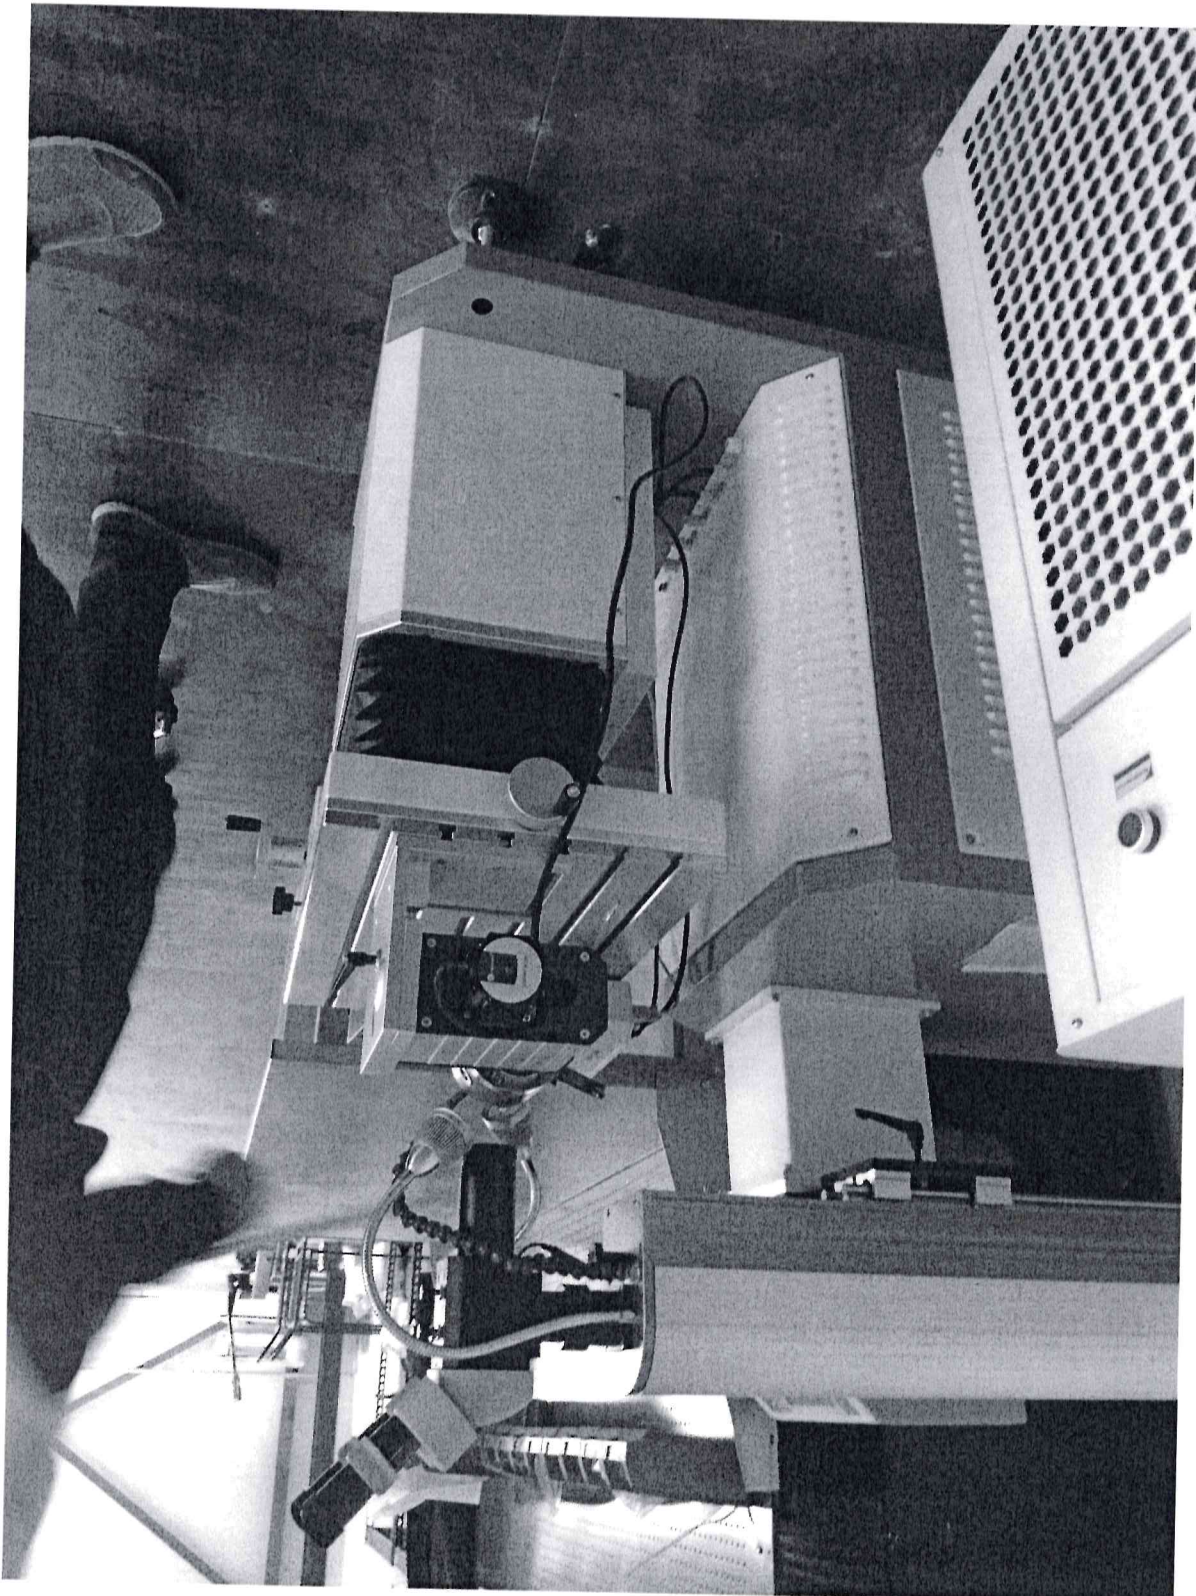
Установка лазерной сварки (вид сбоку)
